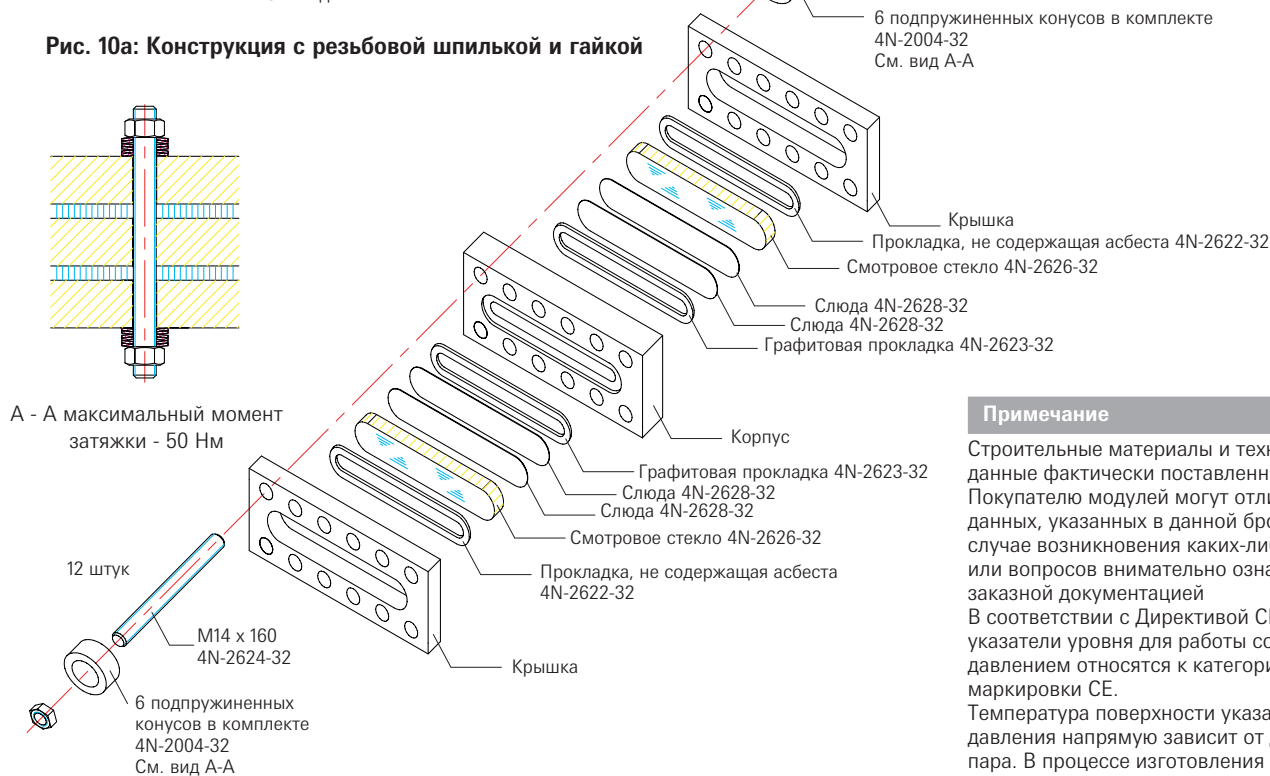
а: Конструкция с резьбовой шпилькой и гайкой
